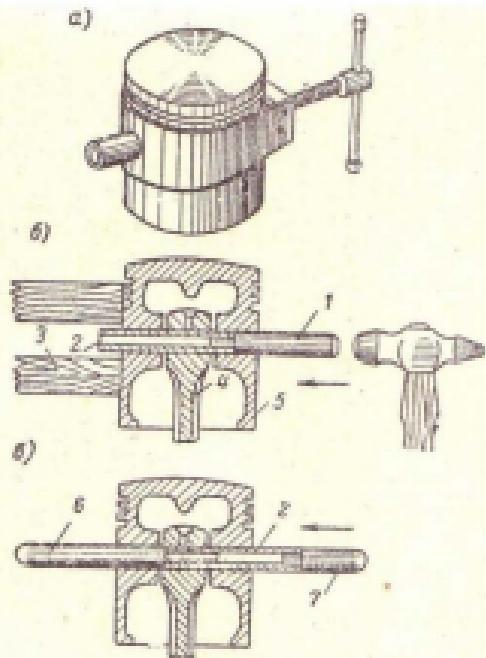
Выпрессовка и запрессовка поршневого пальца с помощью:
